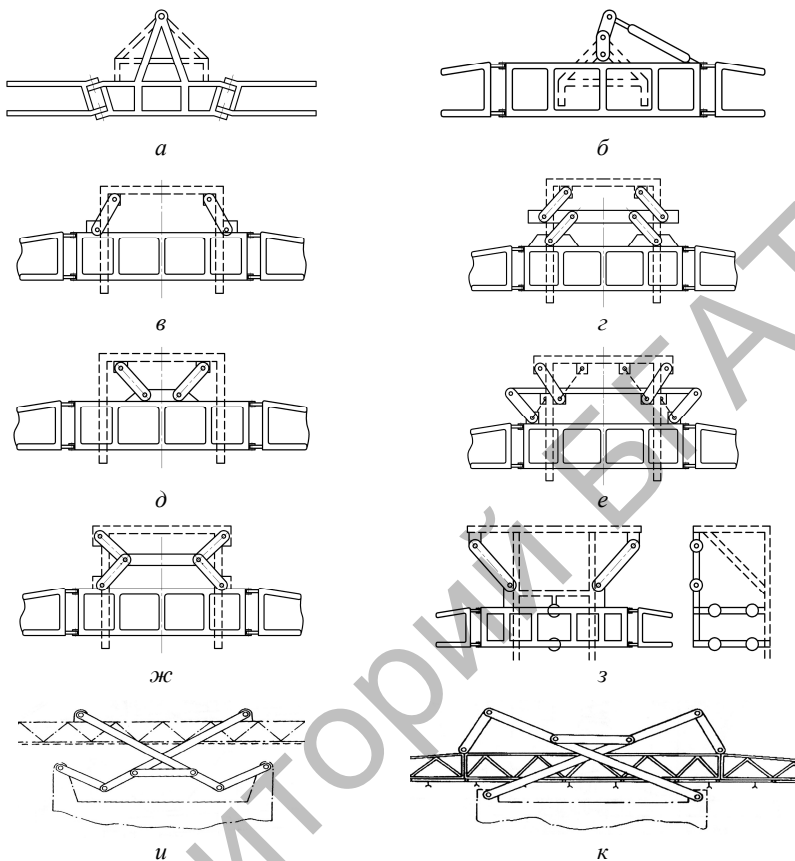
Схемы шарнирно-рычажных маятниковых подвесок штанговых опрыскивателей:
